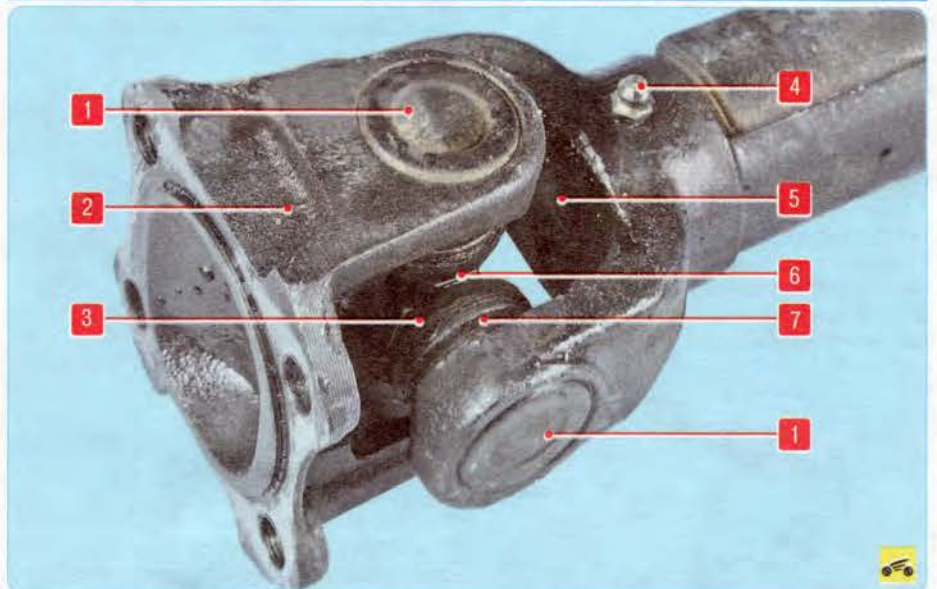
Карданный шарнир: 1 – игольчатый подшипник; 2 – фланец; 3 – манжета, армированная резиной; 4 – пресс-масленка; 5 – заглушка; 6 – крестовина; 7 – стопорное кольцо
